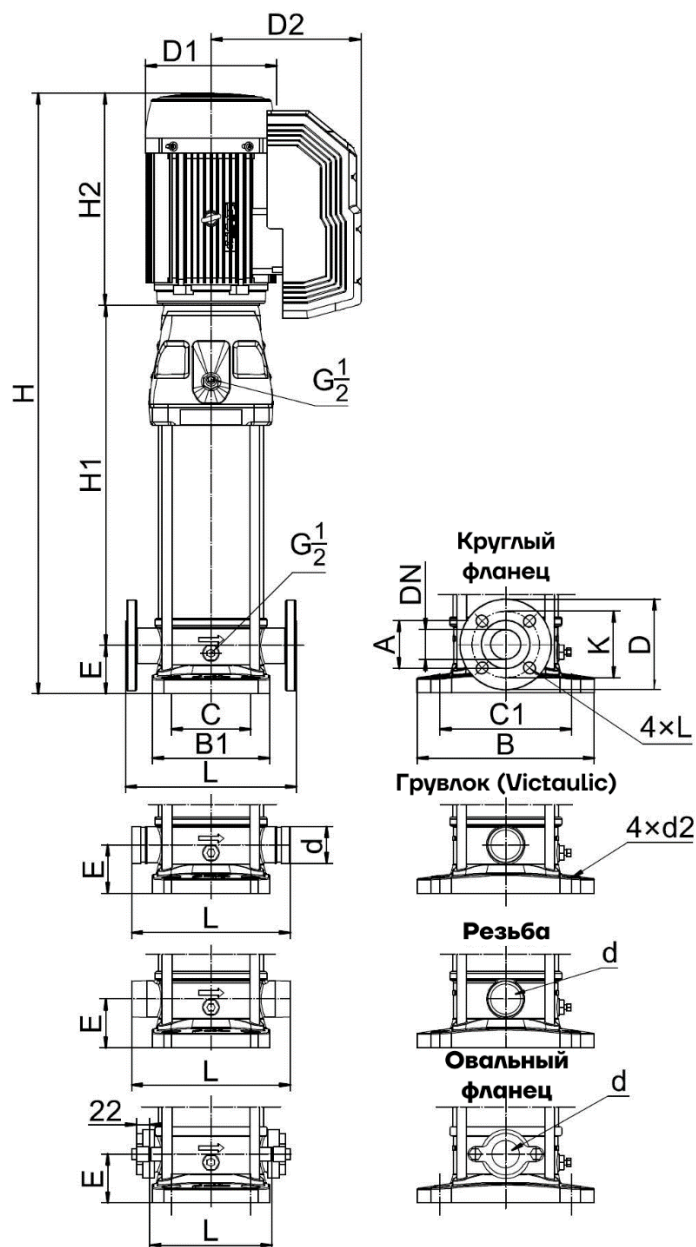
Габаритно-присоединительные размеры CDME/CDMFE
